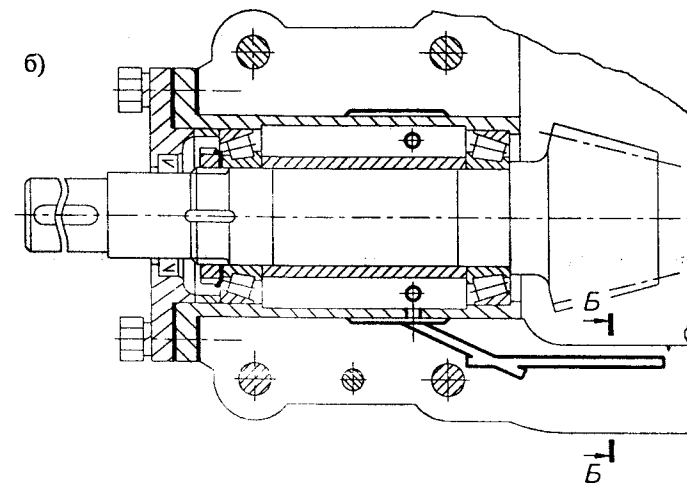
Конструктивные решения по смазыванию подшипников и зубчатых колес редукторов:
